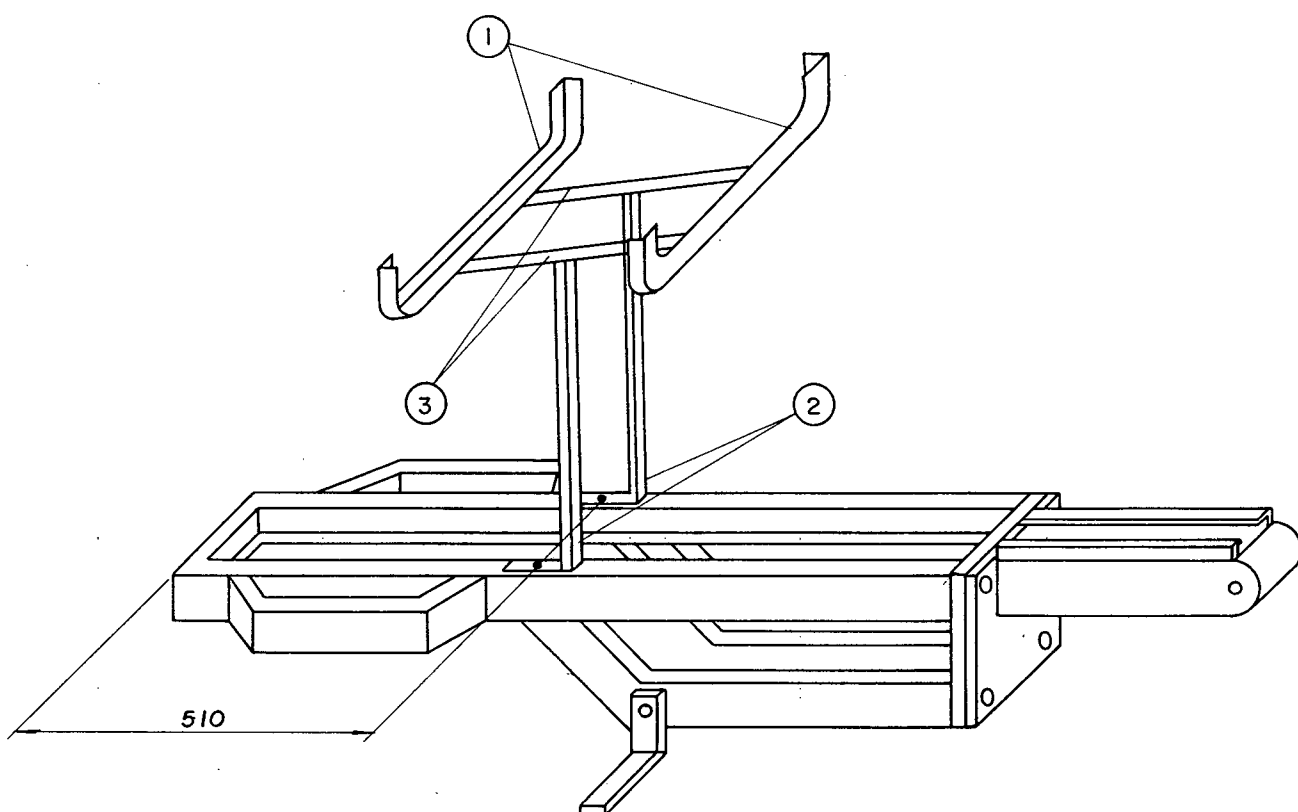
Posição de montagem do suporte da caixa de mudas.
